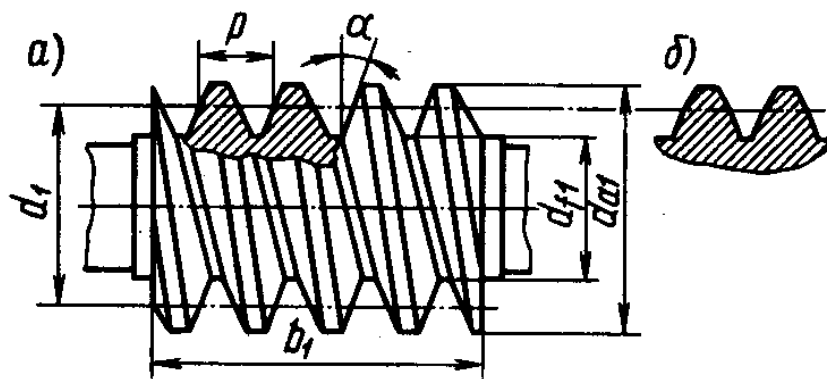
Форма винтовой поверхности цилиндрического червяка:
